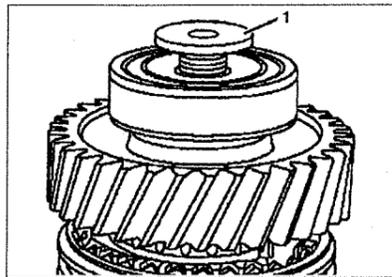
Снятие роликового подшипника (автомобили с двигателями 611.980):
